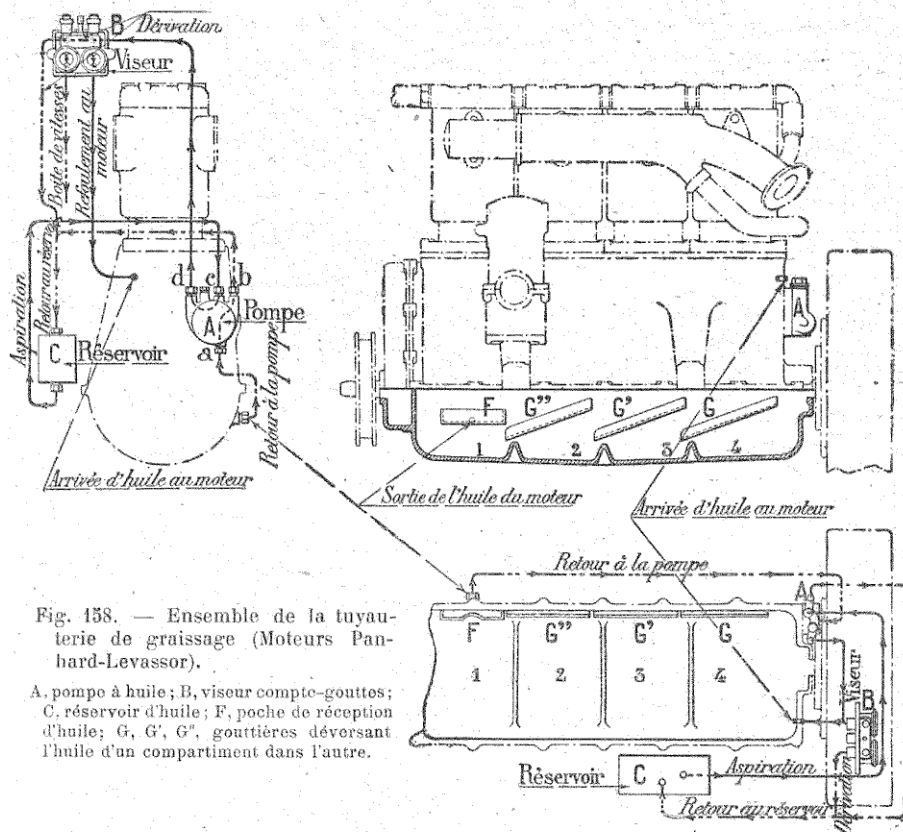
Ensemble de la tuyauterie de graissage (Moteurs Panhard-Levassor).
